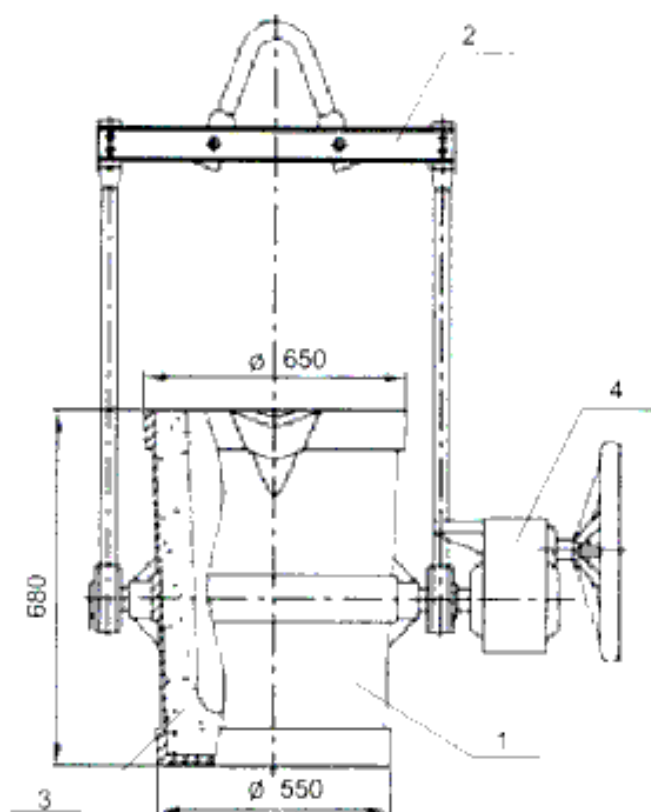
Общий вид разливочного ковша для разливки стали:
